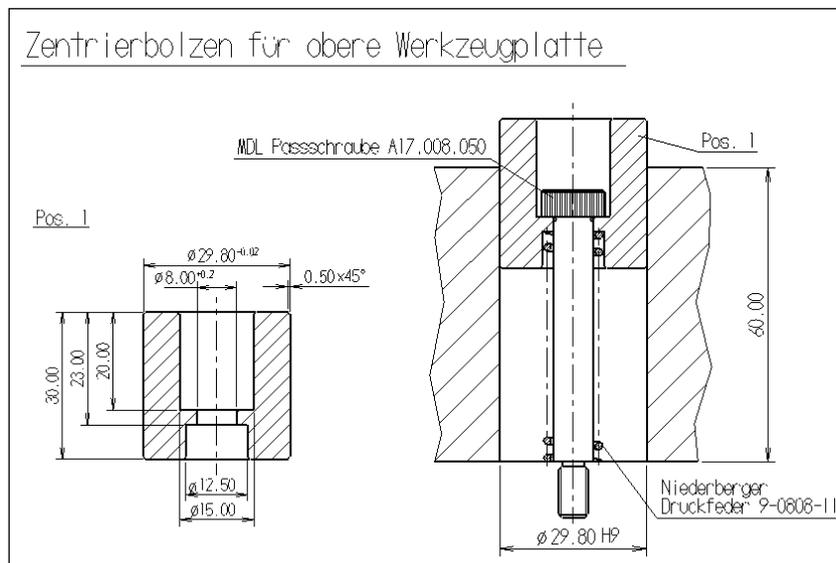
Zentrierbolzen für obere Werkzeugplatte
